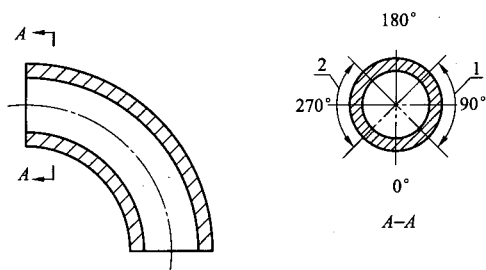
焊接弯头纵向焊缝拼接位置图
